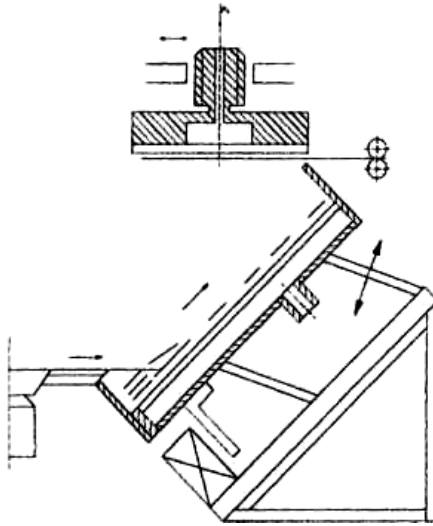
Конструктивна схема вібропневматичного пристрою
